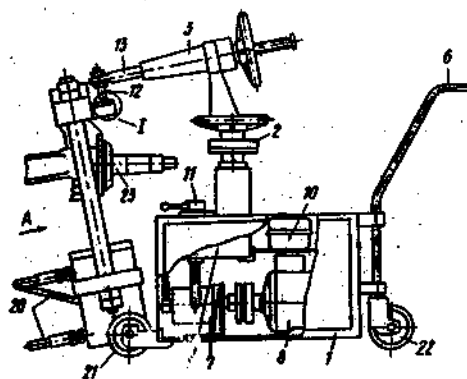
Устройство для выпрессовки шкворней поворотных кулаков автомобилей
